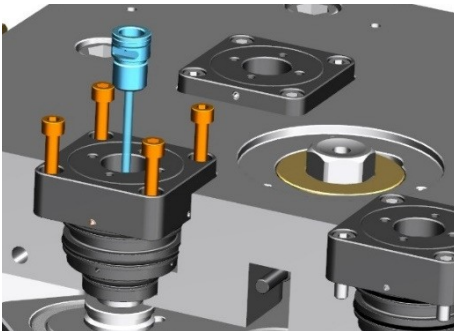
Крепление гидравлического узла и установка держателя клапана
